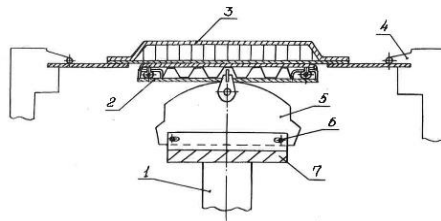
Универсальный пуансон для прессы FEKD: 1 – стол прессы; 2 – гибкая оболочка; 3 – заготовка; 4 – зажим; 5 – сменный шаблон; 6 – фиксатор; 7 – каркас.
